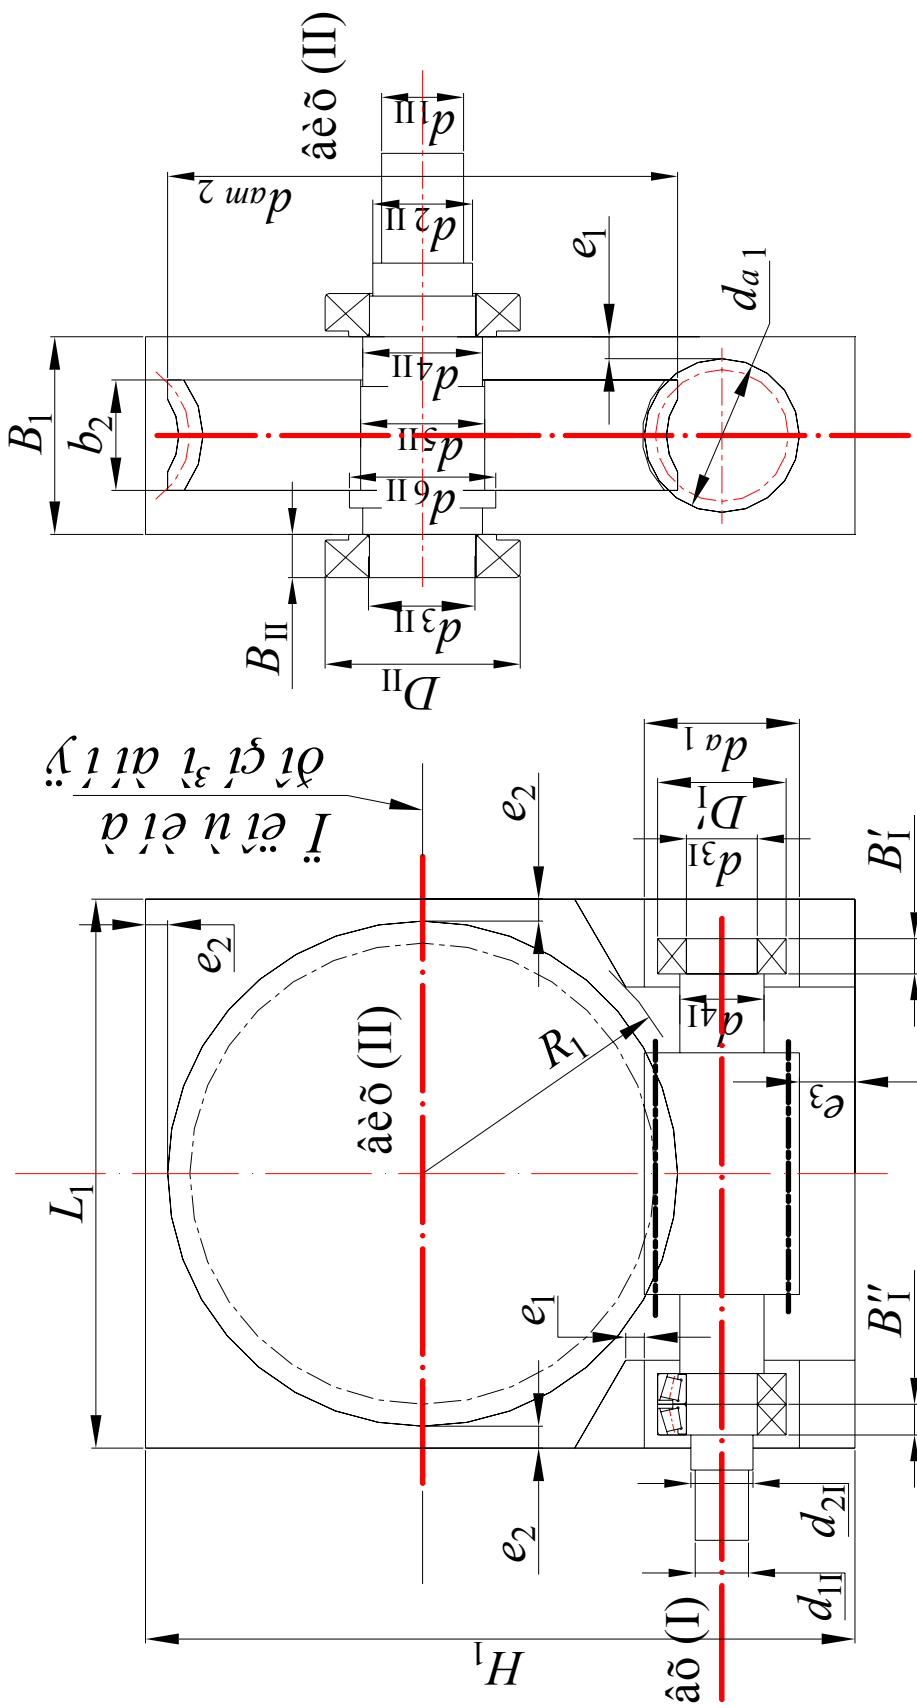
Ескізна компоновка черв'ячного редуктора з нижнім розташуванням черв'яка
